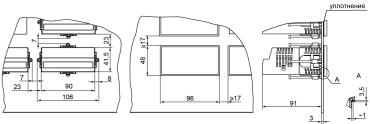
Корпус Щ2 в щите толщиной 3 мм
